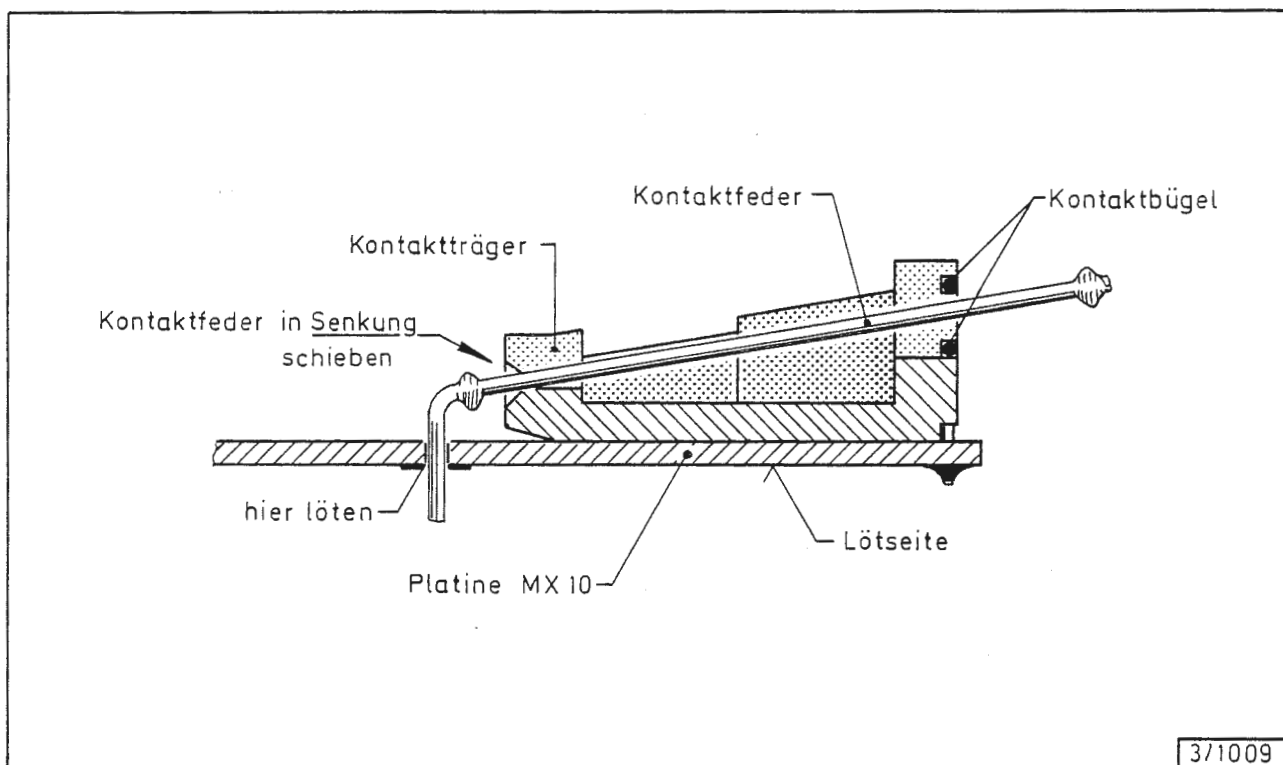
Einspannen der Kontaktfedern (Seitenansicht)
